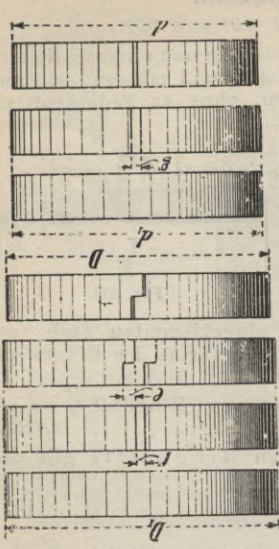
612. Aeusserer Ring. Fig. 613—615. Innerer Ring.
